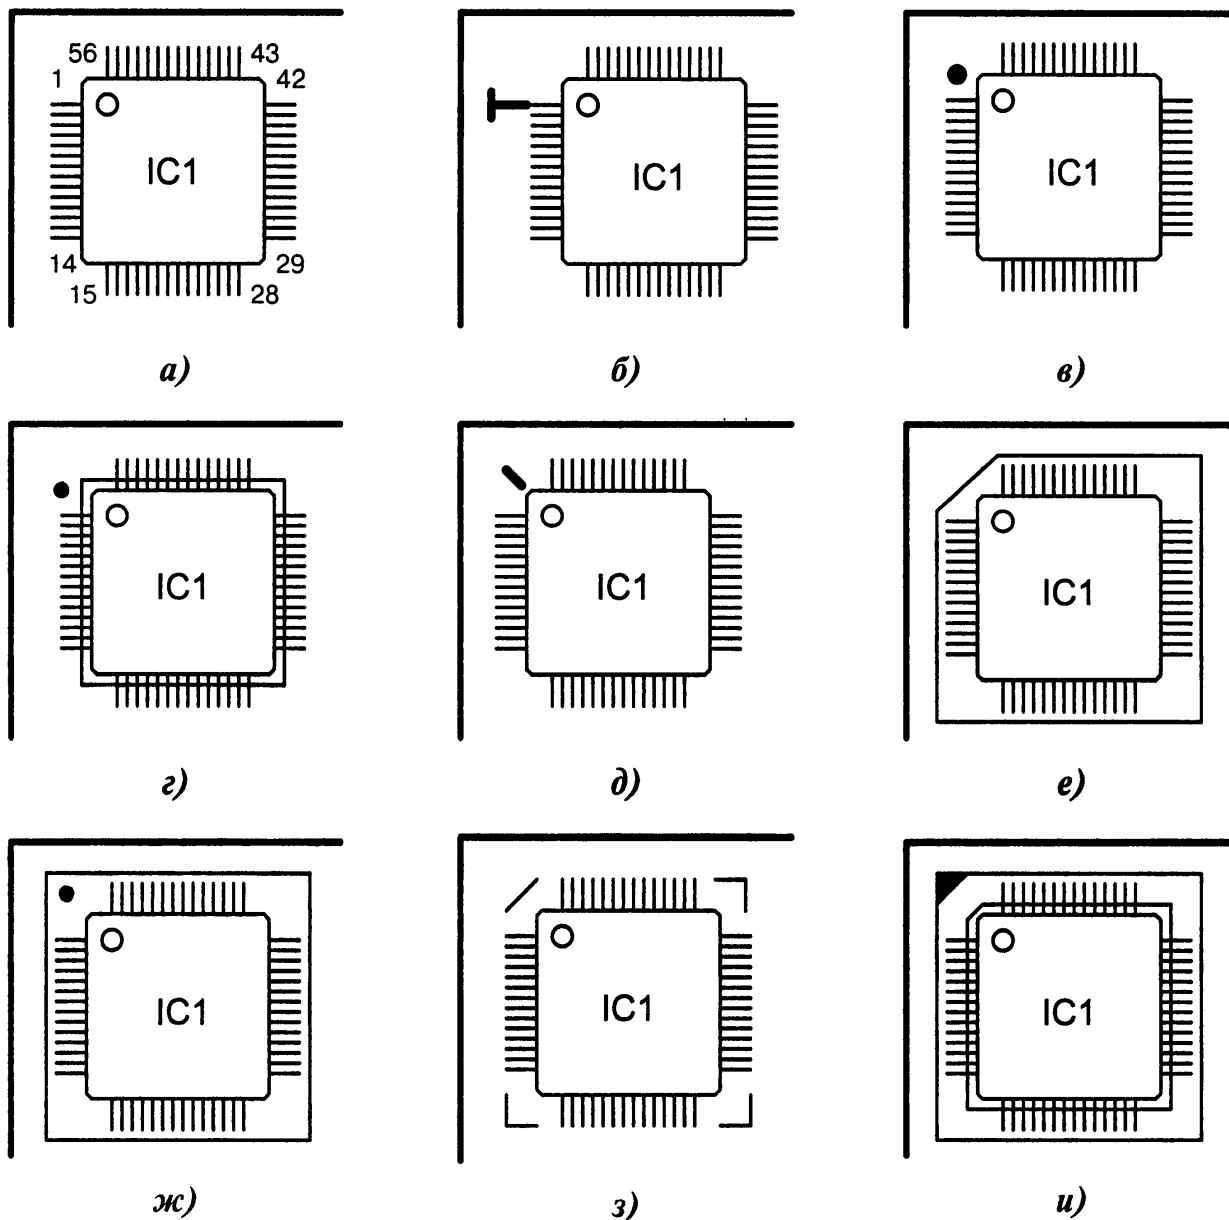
Маркировка микросхем в корпусе TQFP-56 (начало):
